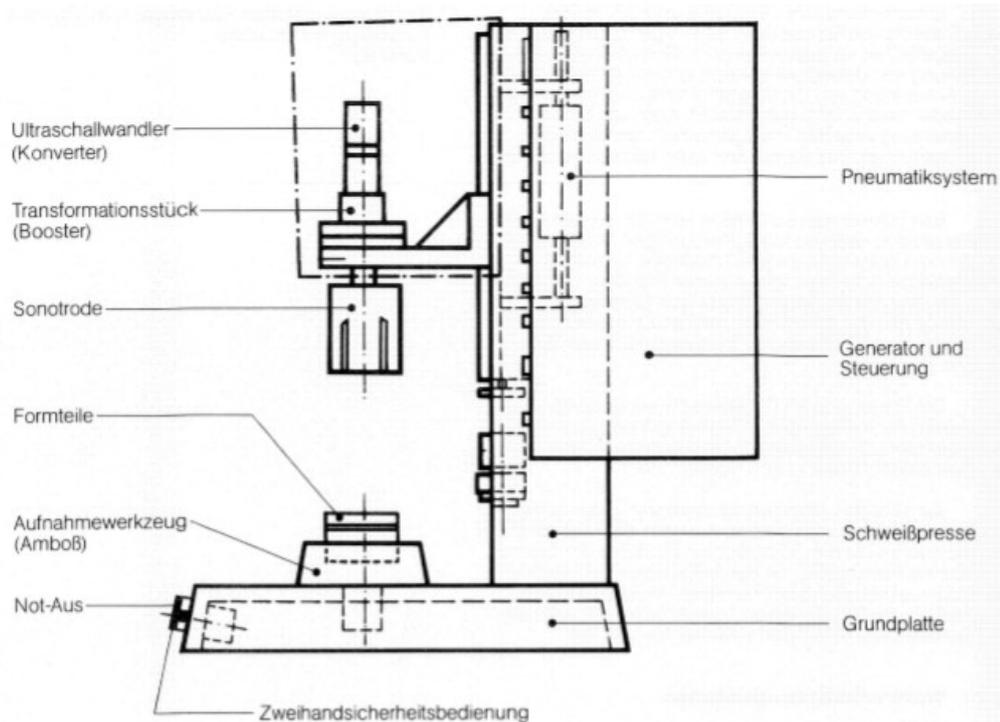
Aufbau einer Ultraschallschweißmaschine [18, S.8]
